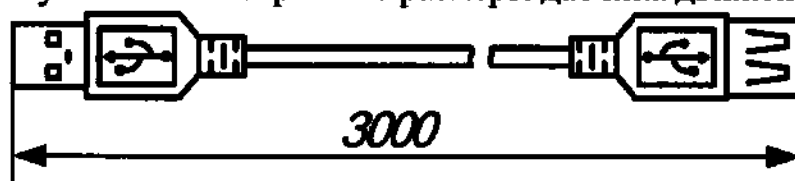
Габаритные размеры соединительного кабеля датчика движения
